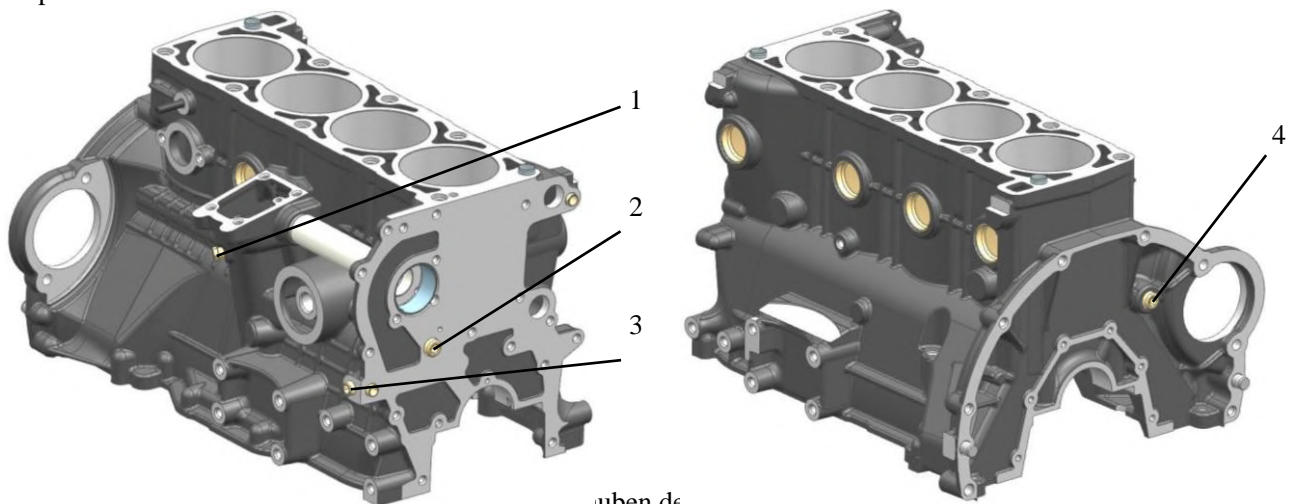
Verschraubungen der Ölkammern des Zylinderblocks.
